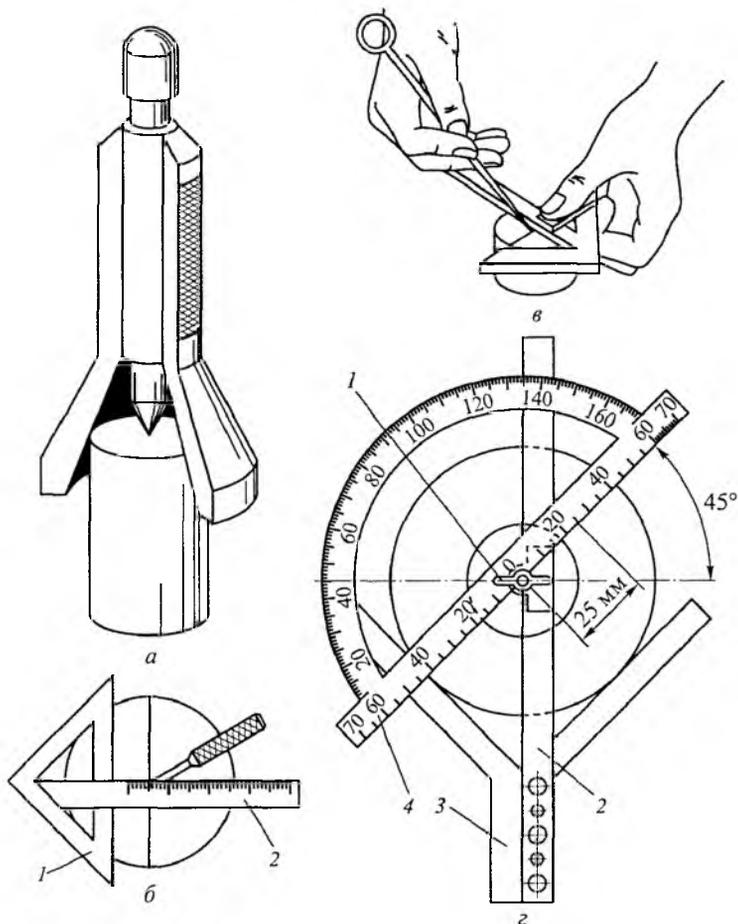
Инструменты для нанесения центровых отверстий:
